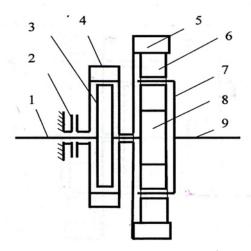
1. Вал двигателя; 2. Муфта; 3. Ротор генератора; 4. Статор генератора; 5. Венец планетарного дифференциала; 6. Сателлиты; 7. Водило; 8. Центральная шестерня; 9. Ведомый вал;
